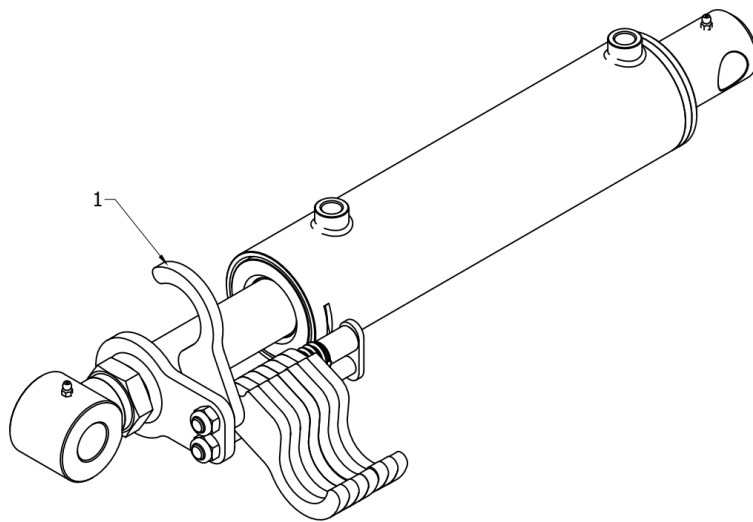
Accrochage correct du premier (1) cliquet sur la tige de piston du vérin pour le réglage de la profondeur de travail de la machine.
